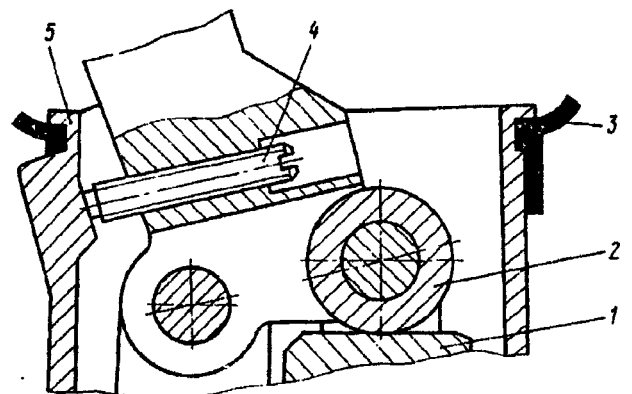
Установка регулировочного винта тормозного двухсекционного крана.
